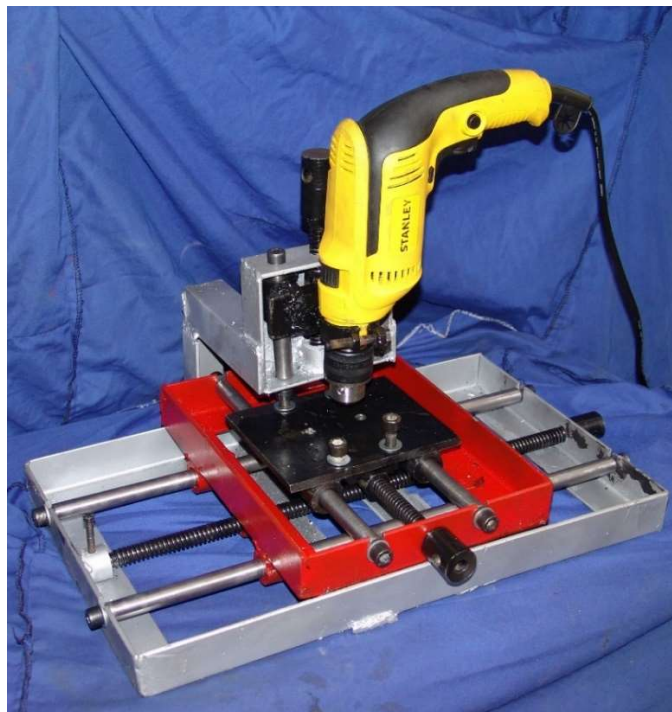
Vue globale de la machine de soudage par friction malaxage.
